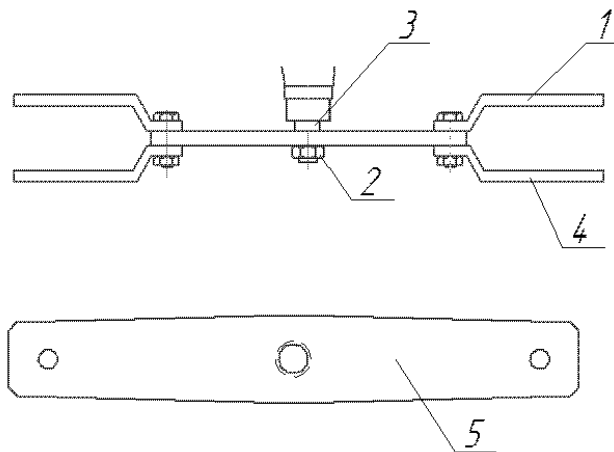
Розроблений різальний апарат з послідовною роботою ножів: 1 – ніж верхній; 2 притискна гайка; 3 – приводний вал; 4 – ніж нижній; 5 – ротор.
